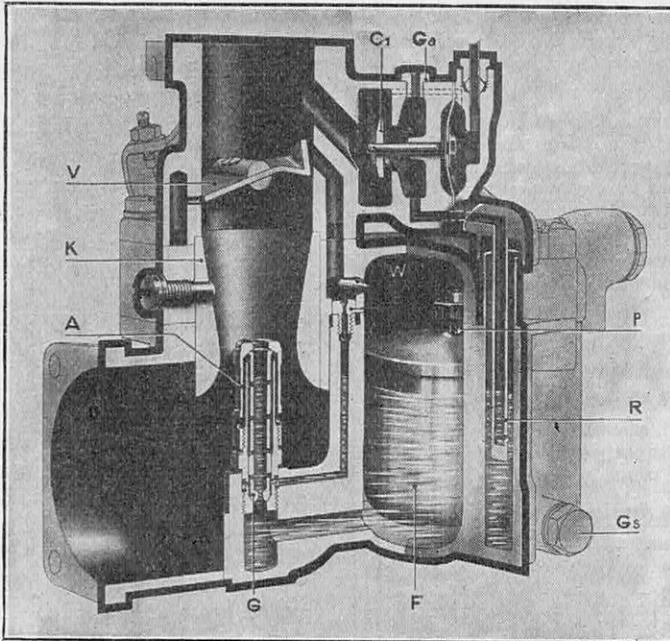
LE CARBURATEUR « SOLEX » A THERMOSTARTER
